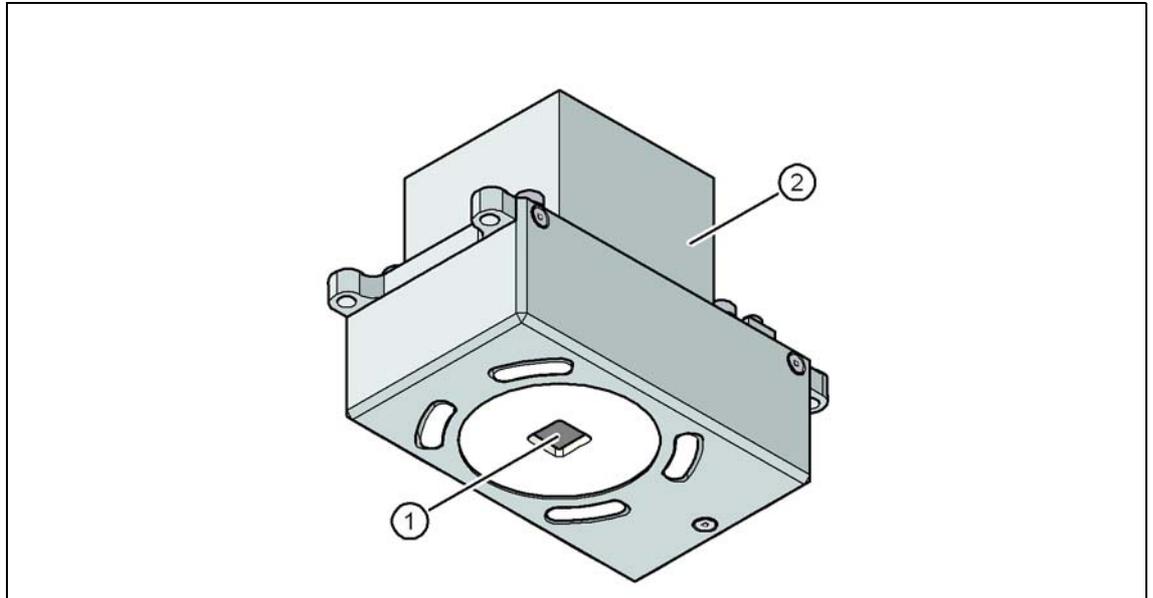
PCB 摄像机 (34 型 , 数字)
